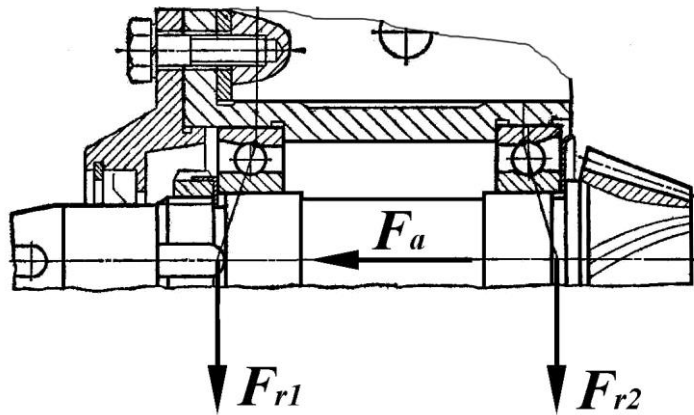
Схема встановлення швидкохідного вала редуктора
